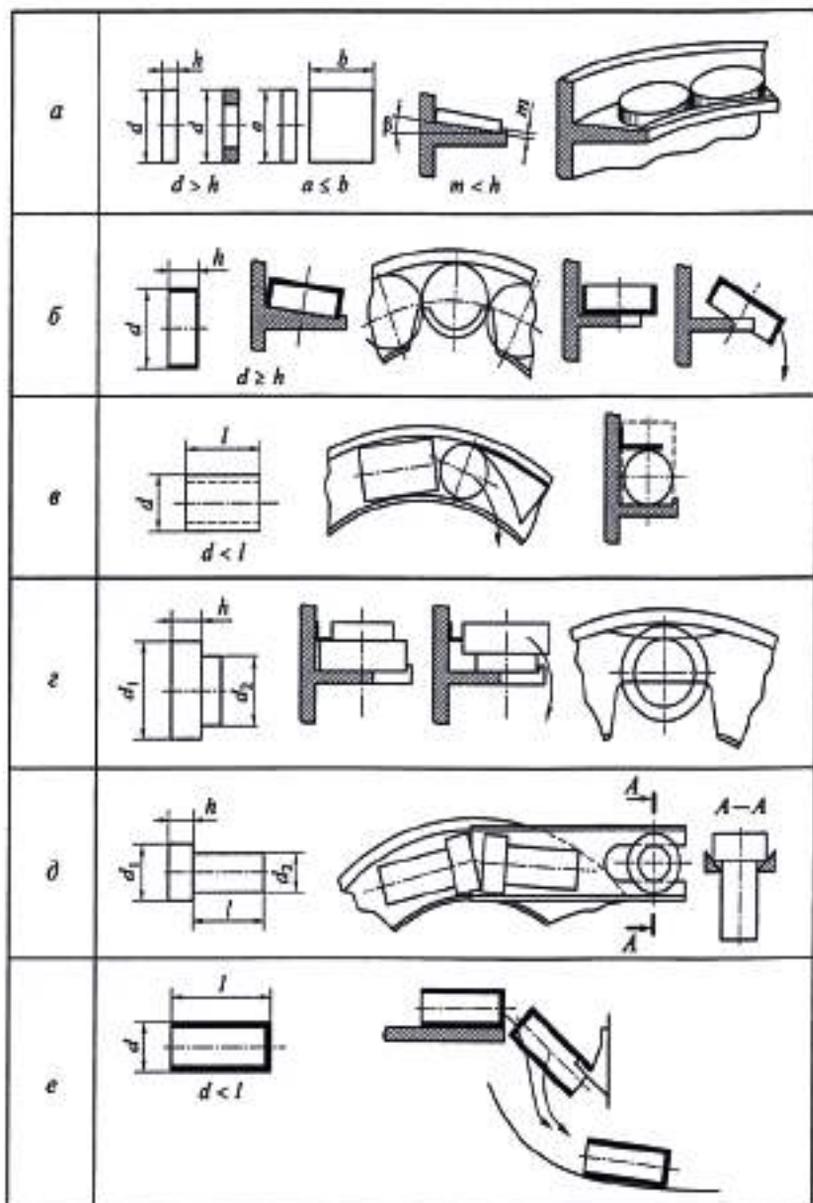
Способы ориентации заготовок в ВЗУ:
